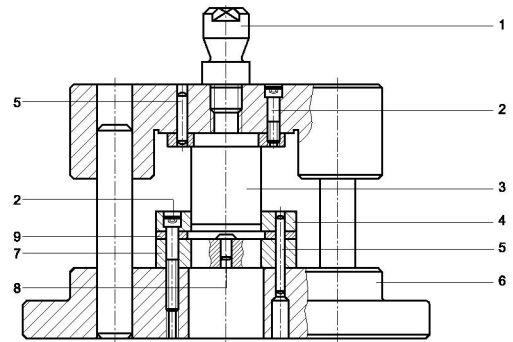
Ausschneidwerkzeug - Säulenführung
